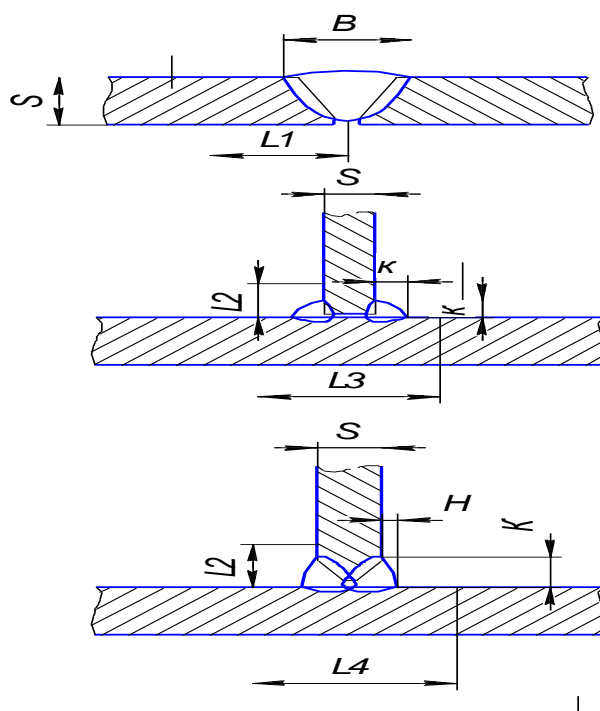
Зачистка кромок свариваемых деталей: L – ширина зачищаемой поверхности; B – ширина шва; K – высота шва; S – толщина детали
